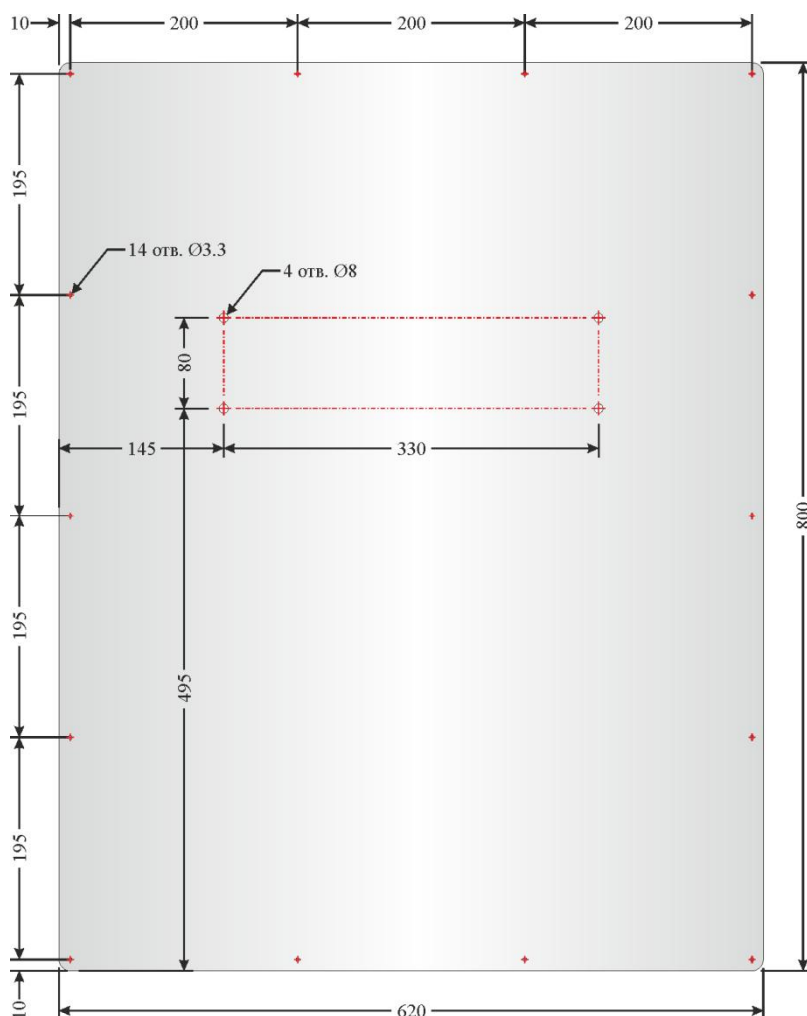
Лист защитный, габаритные размеры и монтажные отверстия
